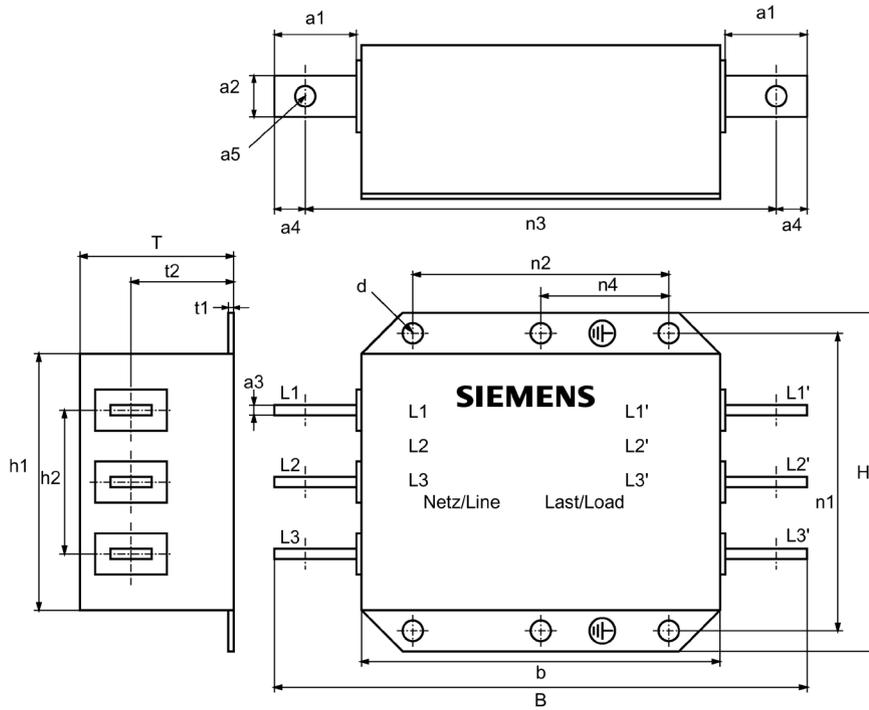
Габаритный чертеж сетевого фильтра
